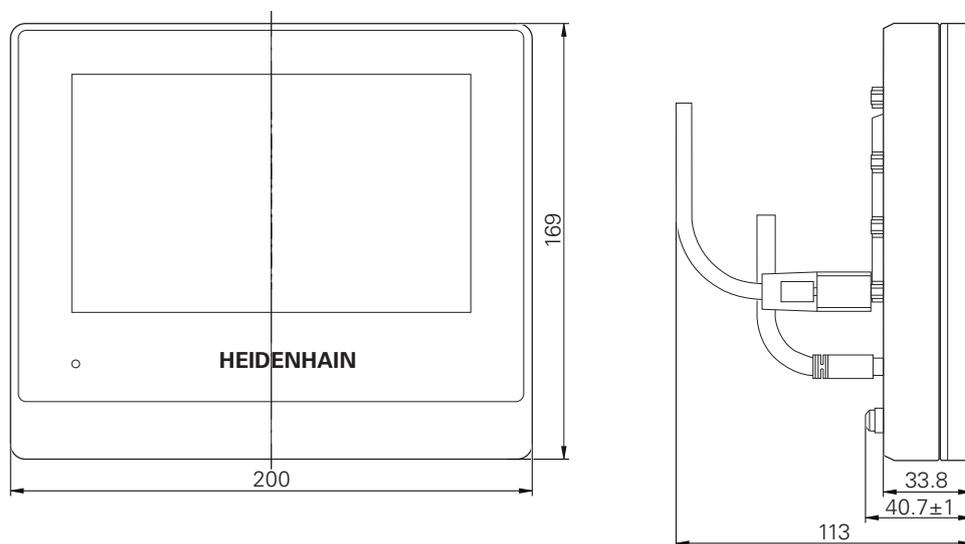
Dimensions du carter des appareils portant le numéro ID 1089178-xx
